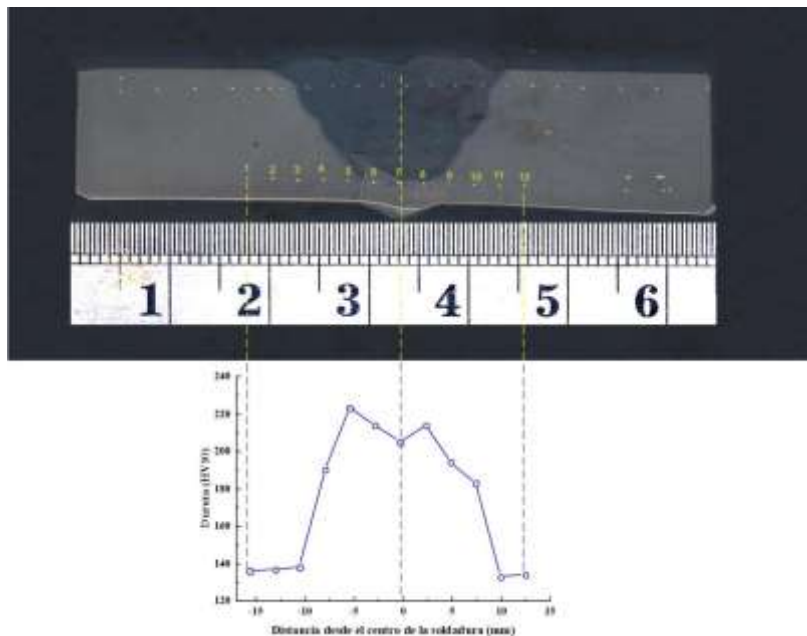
Perfil de dureza medido en la última pasada de soldadura y en el pase de raíz de la junta soldada de acero P5
